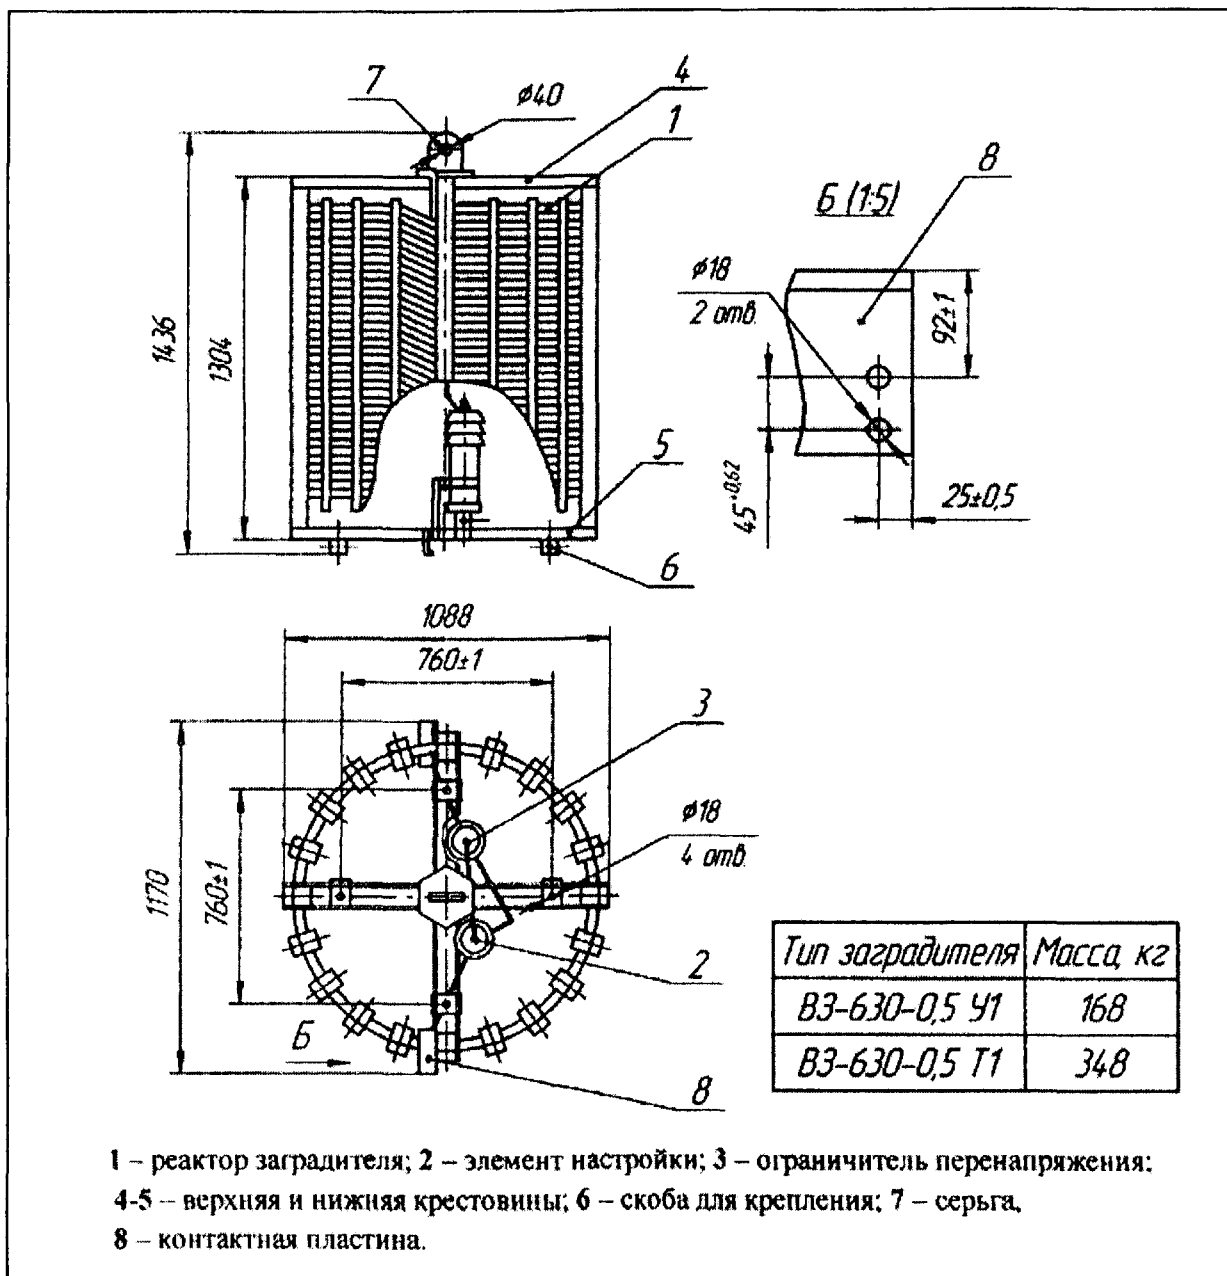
Схемы присоединения и габаритные размеры высокочастотных заградителей типа ВЗ-630-0,5
